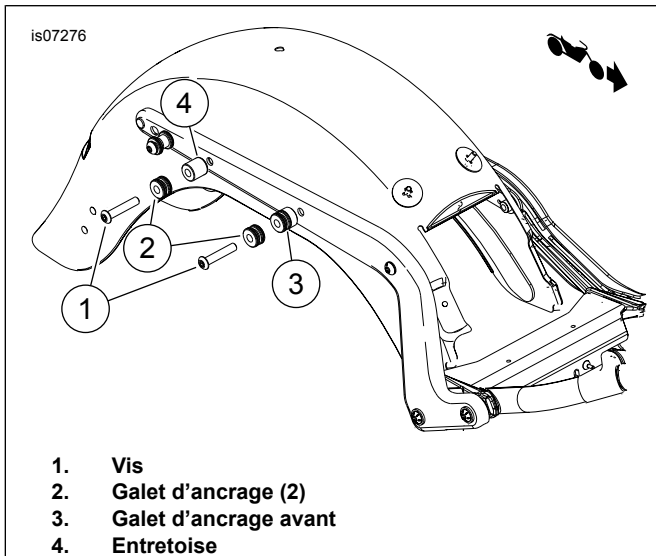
Installation des galets d'ancrage (avec d'autres accessoires amovibles)
